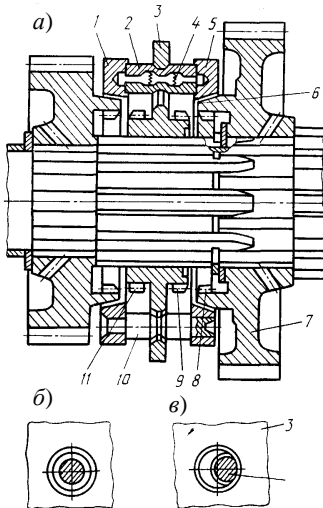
Синхронизатор коробки передач грузового автомобиля:
